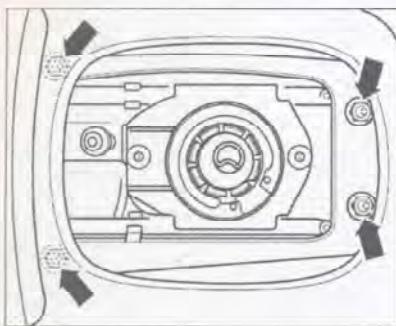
Отверните гайки (стрелки) крепления корпуса механизма переключения передач.
